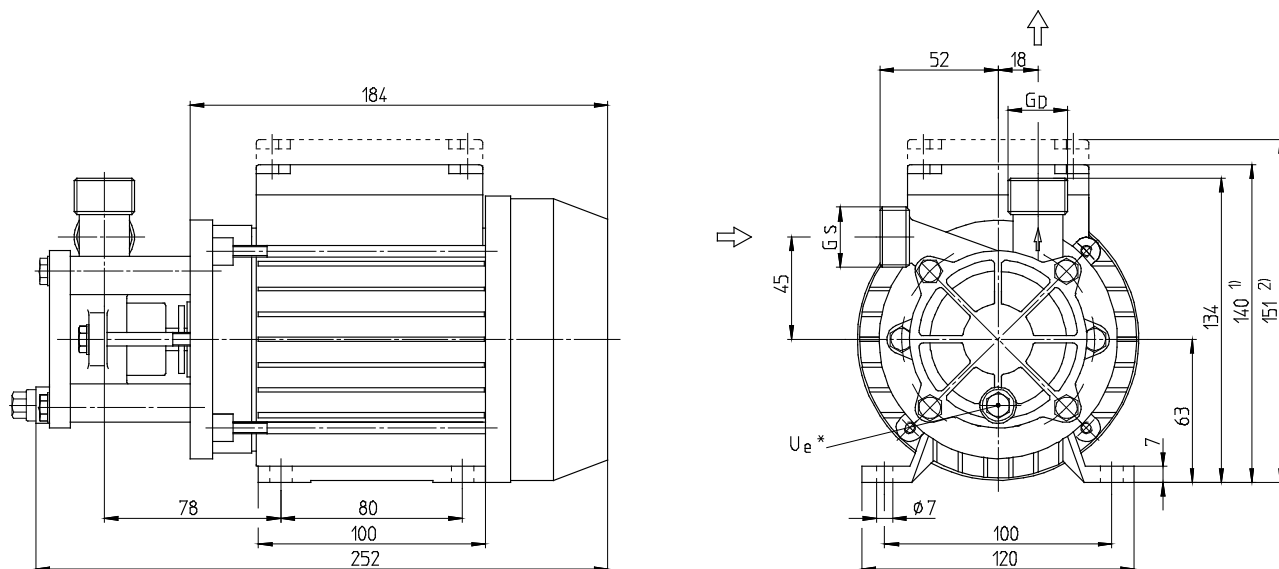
Maßzeichnung NPY-2051 selbstansaugend
